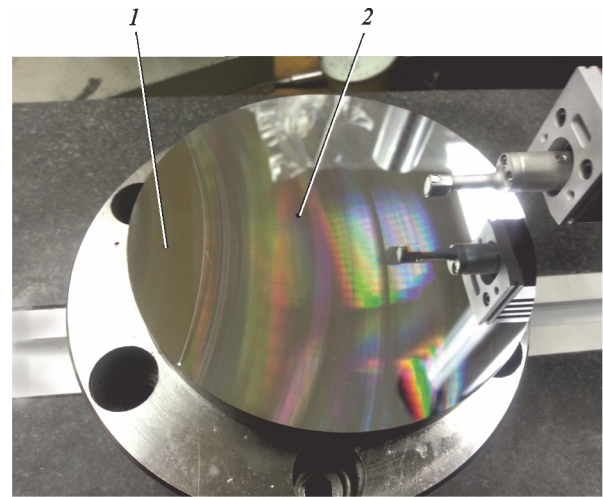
Контроль с помощью профилометра шероховатости поверхности, обработанной неизношенным (1) и изношенным (2) резцами
